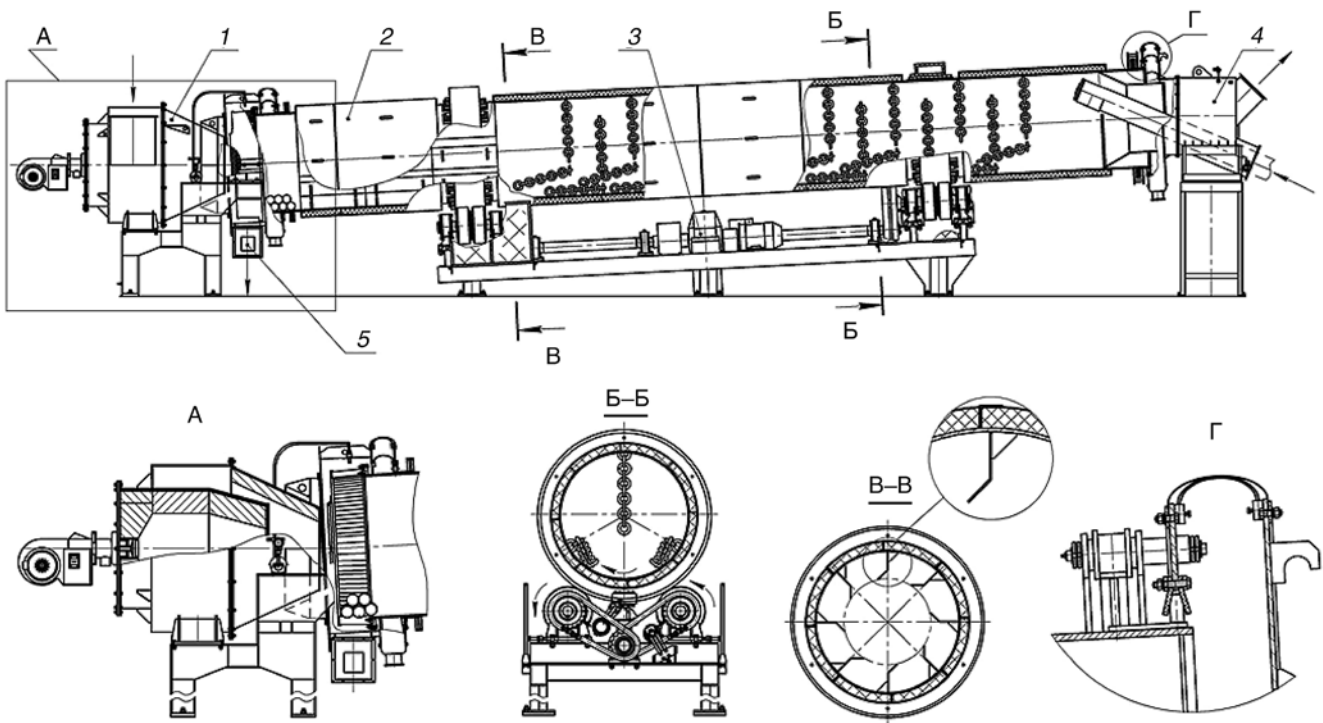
Схема сушильного барабана: 1 – тепловой агрегат; 2 – барабан; 3 – привод; 4 – загрузочный короб; 5 – камера выгрузки
